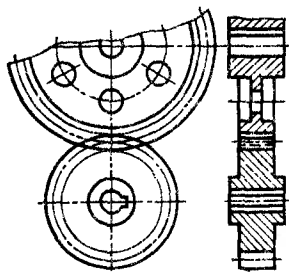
Цилиндрическая передача с внешним зацеплением
